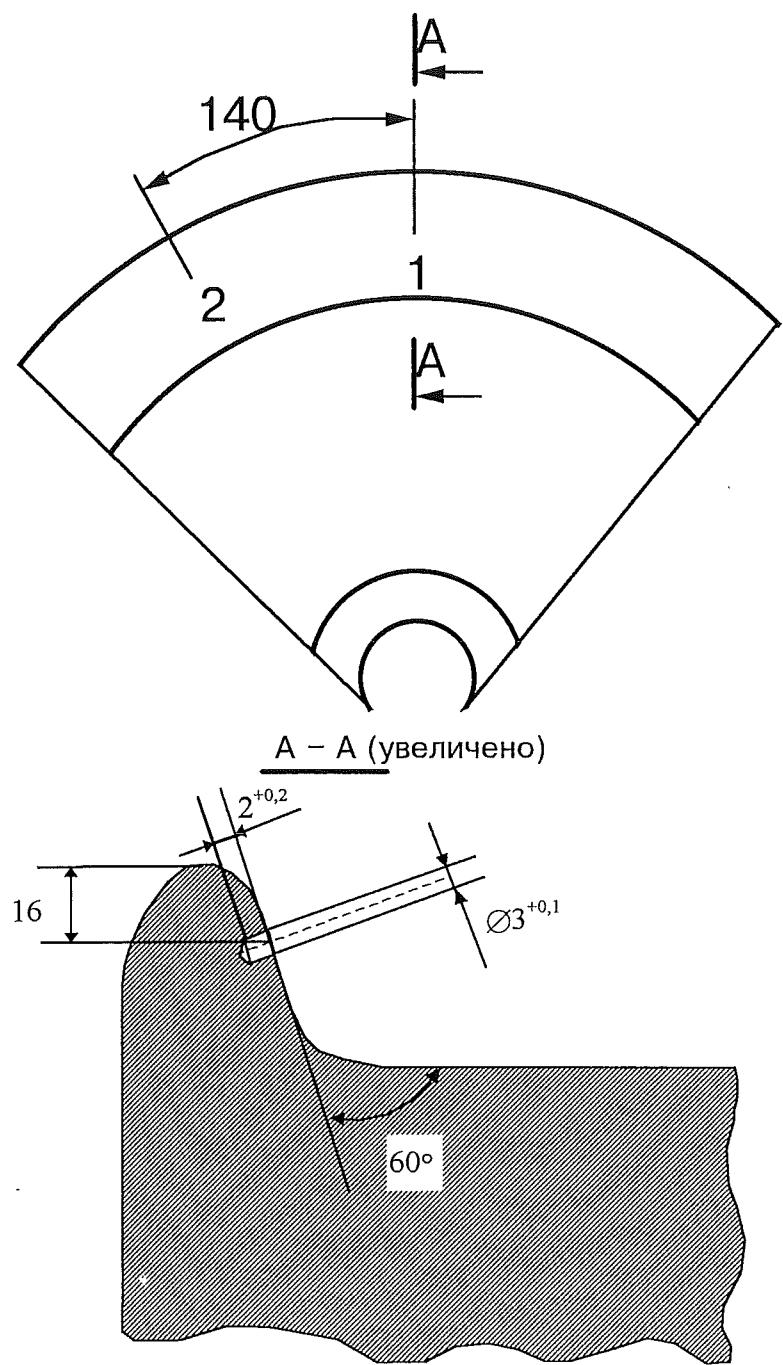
Контрольный образец типа 07.09.05
